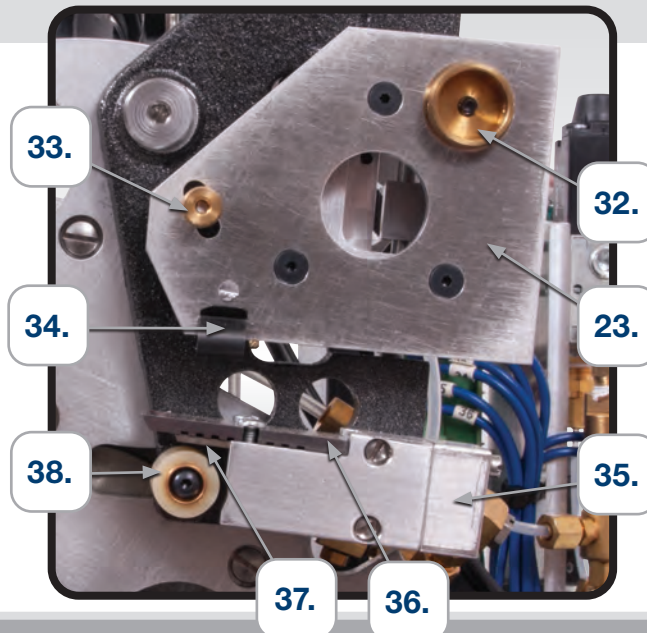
ENSEMBLE DE PLAQUE FRONTALE – VUE AVANT
